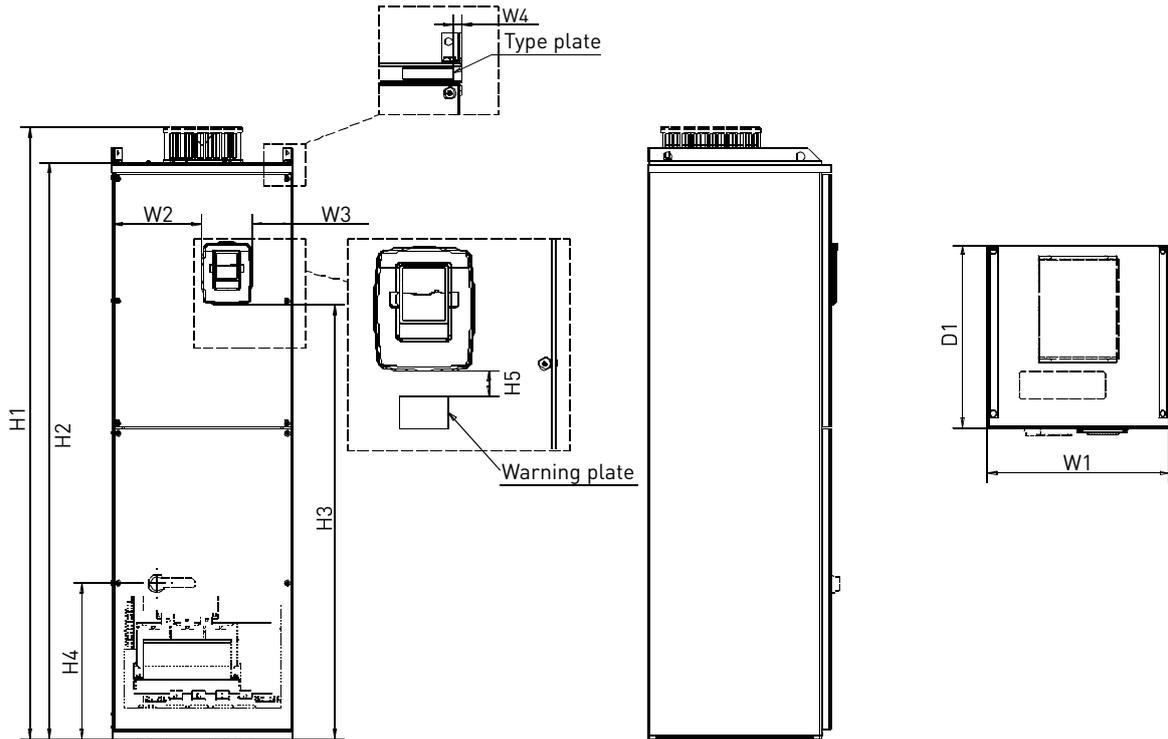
FR10 和 FR11 变频器 (立式单元) 的尺寸
